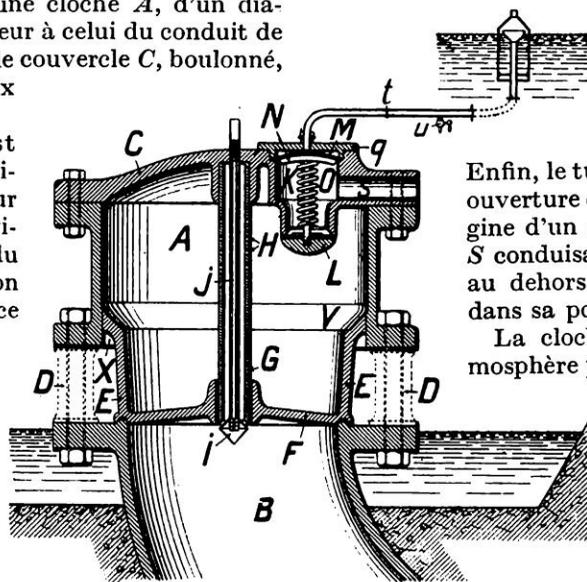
COUPE DU RÉGULATEUR DE NIVEAU
